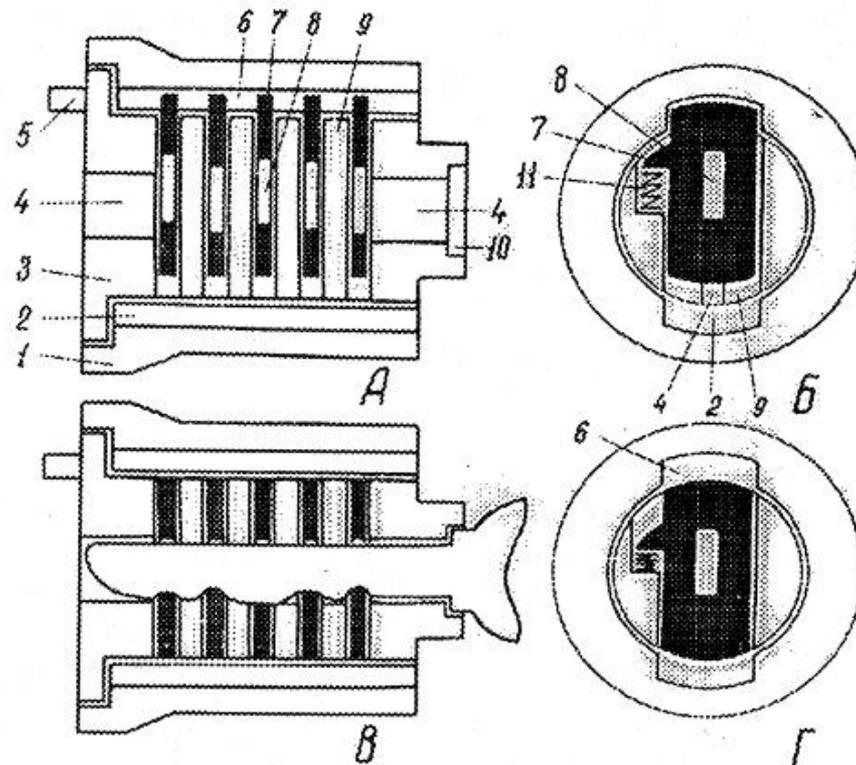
Устройство цилиндрического механизма с поперечным расположением пластинок в цилиндре: А, Б — цилиндрический механизм в запертом положении; В, Г — цилиндрический механизм в отпертом положении; 1 — корпус; 2 — нижний паз корпуса; 3 — цилиндр; 4 — скважина для ключа; 5 — поводок; 6 — верхний паз корпуса; 7 — пластинка; 8 — окно в пластинке; 9 — перемычка; 10 — заплечико для упора ключа; 11 — пружина
